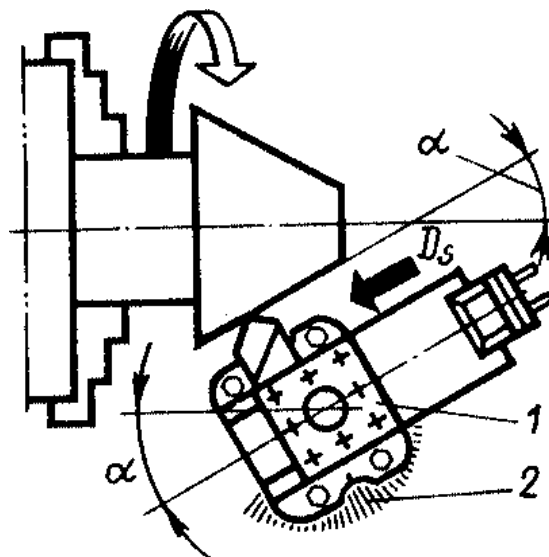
Схема обработки наружной конусной поверхности способом поворота верхней части суппорта:
